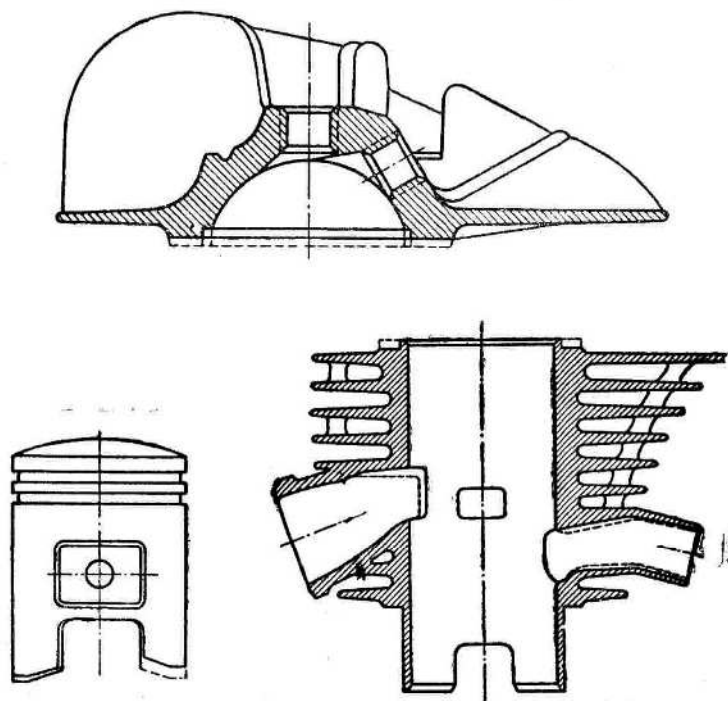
Головка цилиндра, поршень и цилиндр двигателя М1Е
